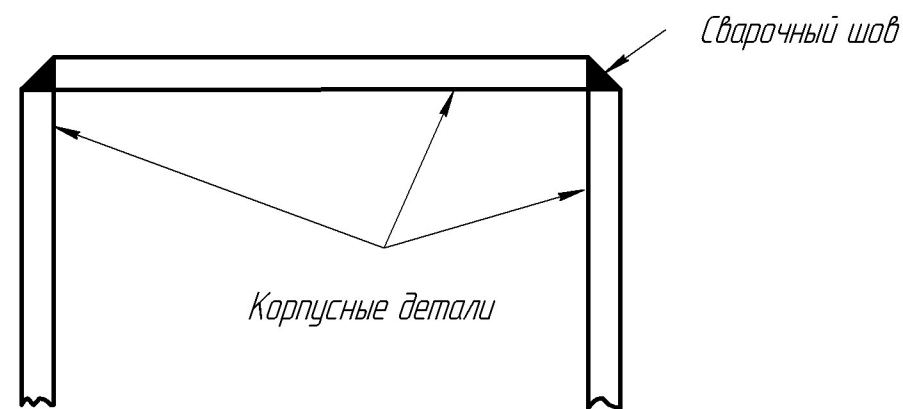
Сопряжение корпусных деталей СБО при сварке.
